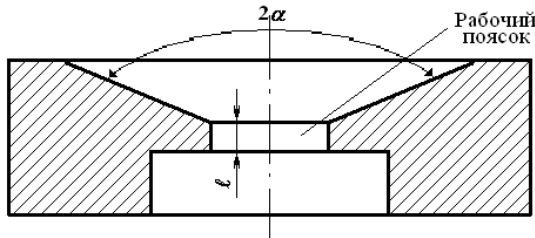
Сечение типовой матрицы: 2α – угол при вершине конуса матрицы, рад; ℓ – длина цилиндрической части отверстия матрицы, м
